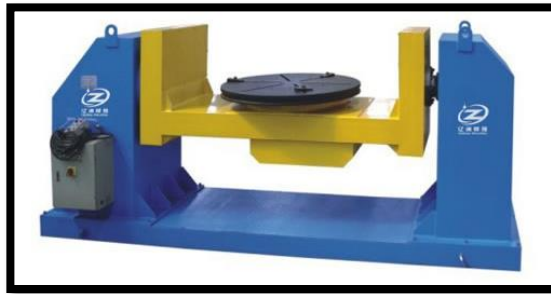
Dispositivo de sujeción y giro, posicionado horizontal.
